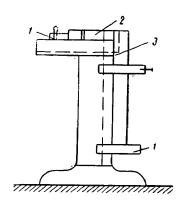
Приспособление для вставки петушков в шлицы коллекторных пластин:
